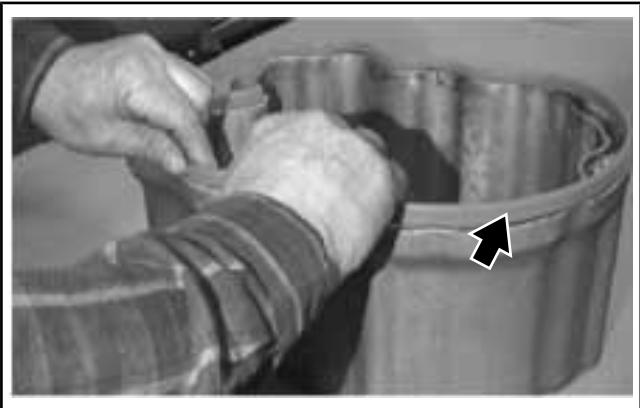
Установка уплотнительной прокладки крышки клапана
